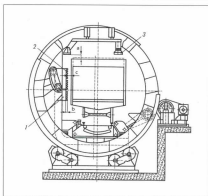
Общий вид и схема вагоноопрокидывателя роторного типа
